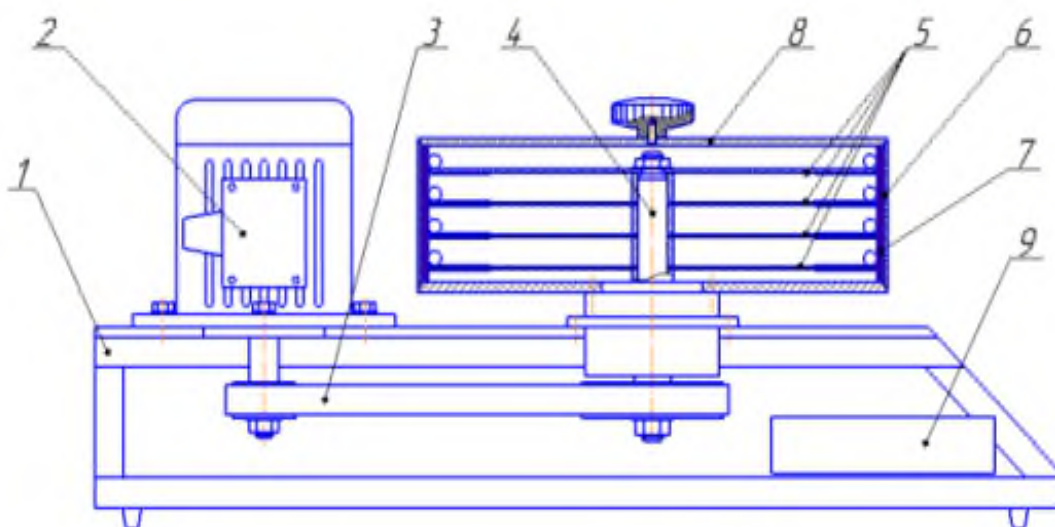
Схема устройства для много инструментальной центробежной абразивной обработки
